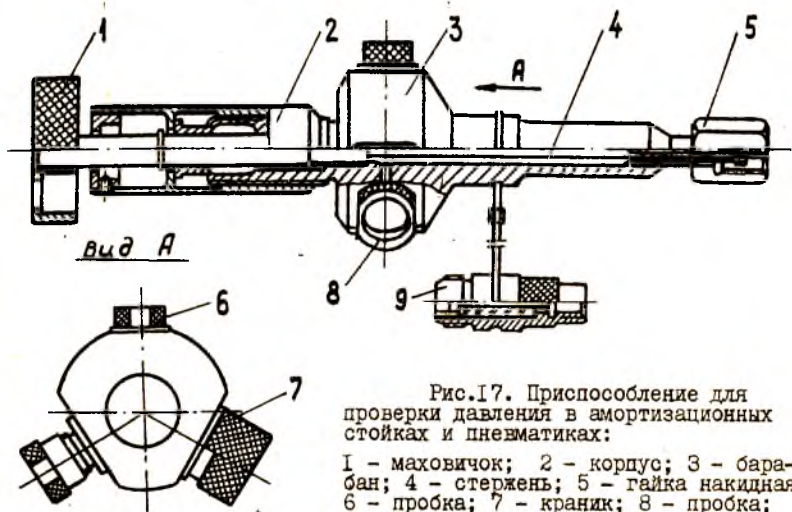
Приспособление для проверки давления в амортизационных стойках и пневматиках:
